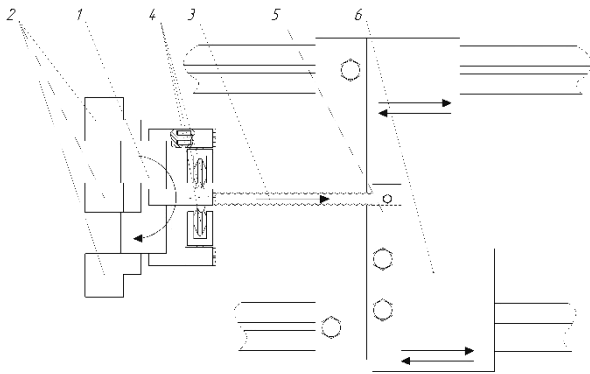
Схема роботи оснащення для профілювання гвинтоподібних труб обкатною головкою з планетарним обертанням роликів: 1 – трьохроликів обкатна головка, 2 – патрон токарно-гвинторізного верстату, 3 – труба-заготовка, 4 – ролики, 5 – тримач, 6 – супорт, 7 – притискальна планка
